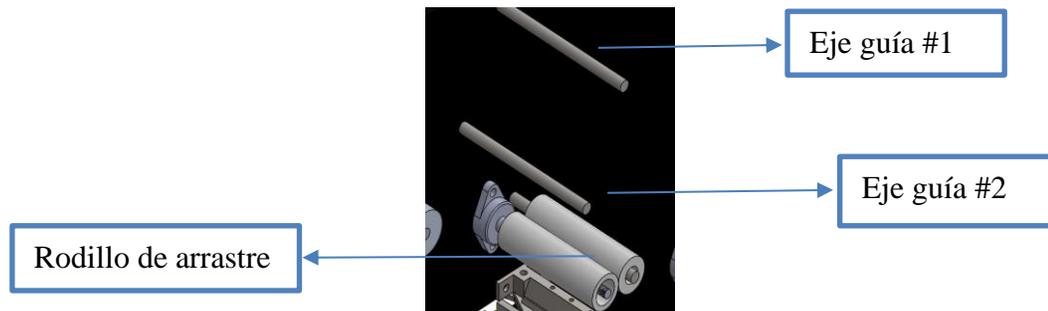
Diseño etapa de enrollado diseño virtual en software SolidWorks.
